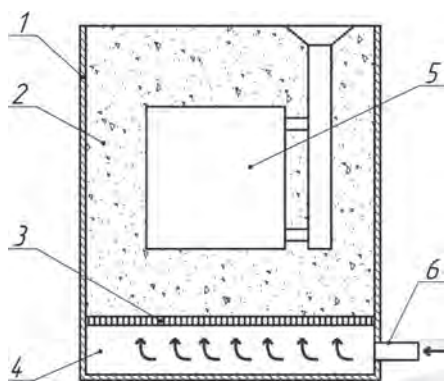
Схема охлаждения отливки в контейнере: 1 – контейнер; 2 – песок; 3 – перфорированное дно; 4 – полость; 5 – отливка; 6 – штуцер
